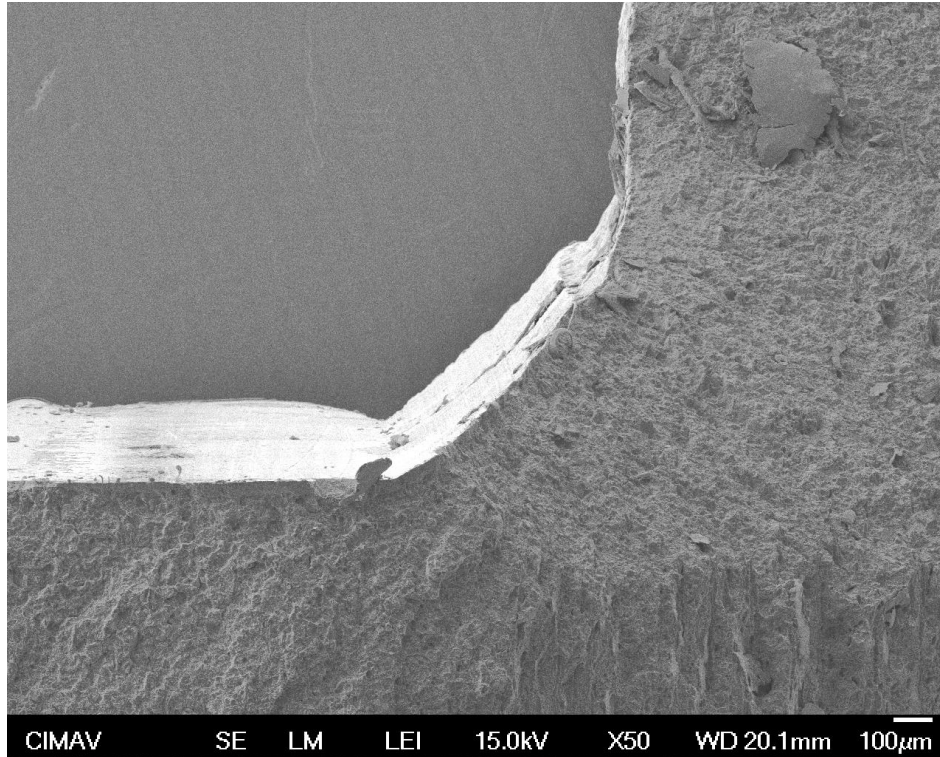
Superficie de fractura de la mordaza # 1, esquina superior izquierda, mostrando que fractura es del tipo dúctil, (4,000 X).
